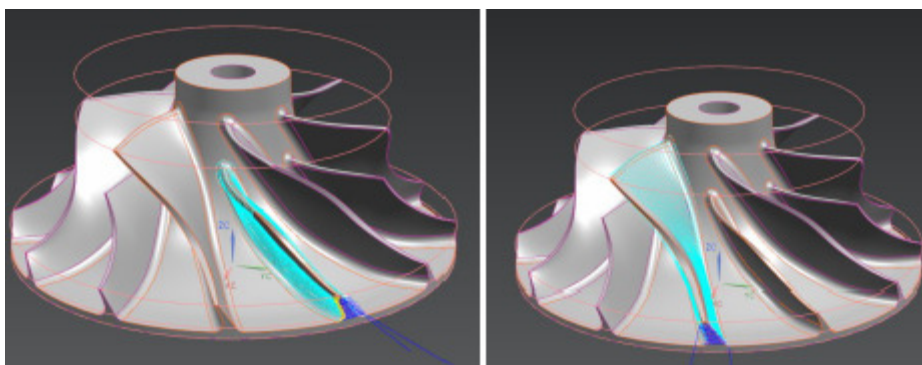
Álabes de un plato de impellers: *splitter* (izquierda) y *blade* (derecha)
